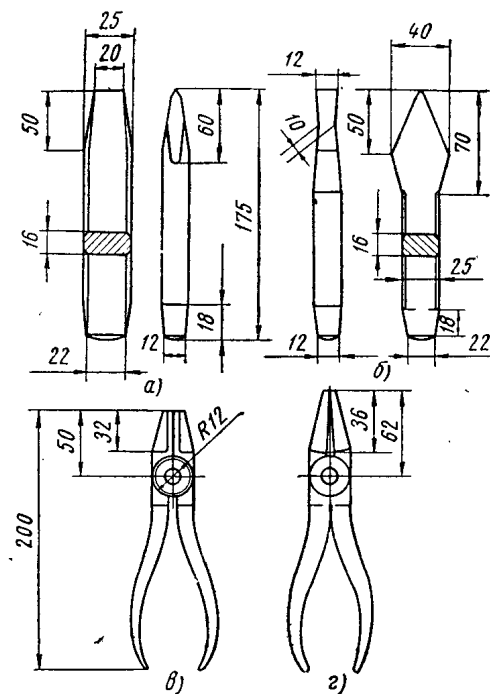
Слесарный инструмент, изготовленный ковкой:
